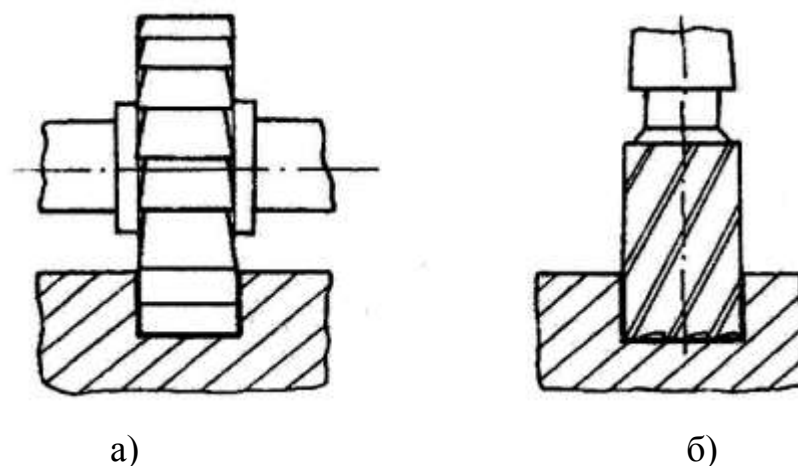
Фрезерование пазов дисковыми (а) и концевыми (б) фрезами
